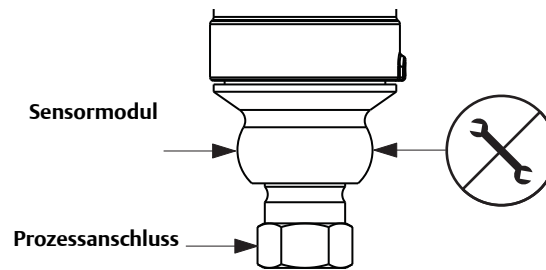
Niederdruckanschluss des In-Line Messumformers für Überdruck
